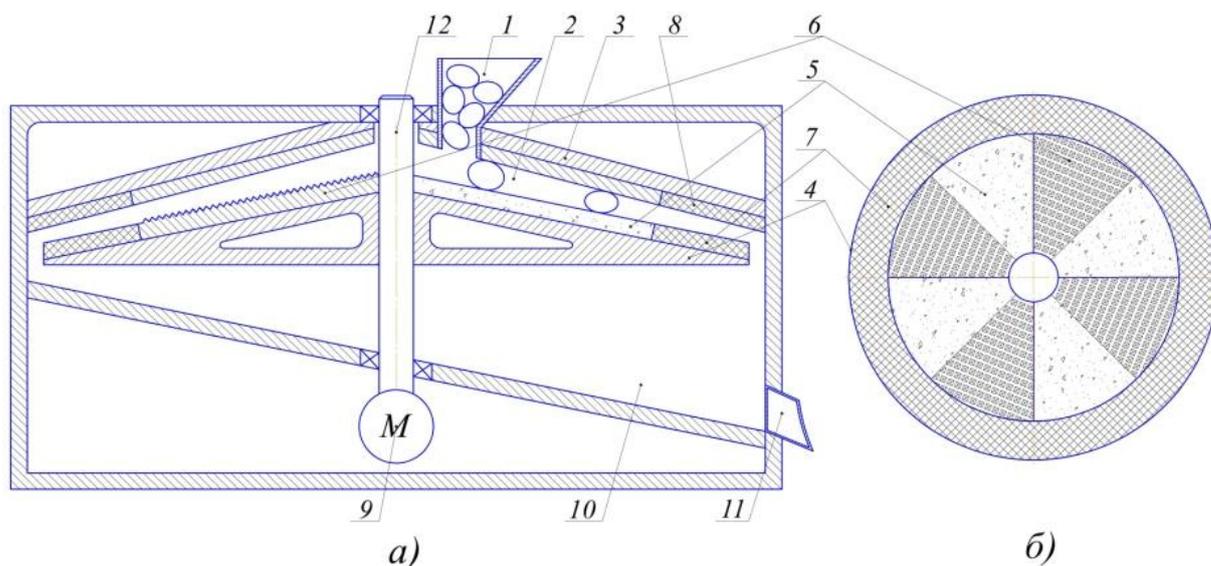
Устройство для извлечению ядер из кедрового ореха:
